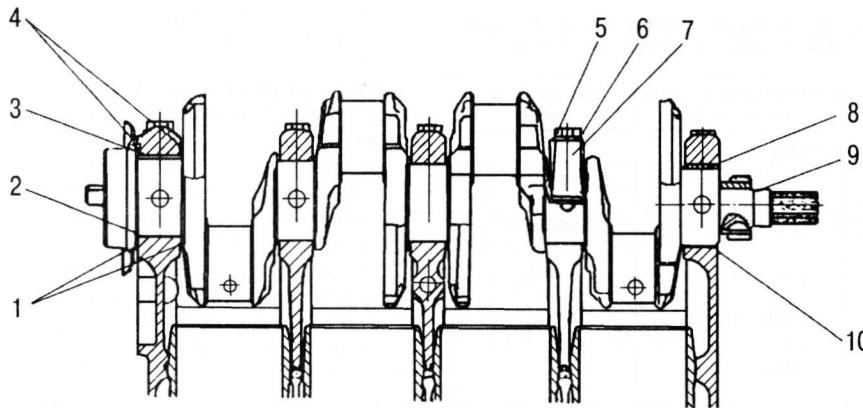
Укладка коленчатого вала в блок: 1, 4 – упорные полукольца; 2 – пятый коренной подшипник; 3 – крышка пятого коренного подшипника; 5 – болт крепления крышки коренного подшипника; 6 – шайба; 7 – крышки коренных подшипников; 8, 10 – вкладыши коренных подшипников; 9 – коленчатый вал
